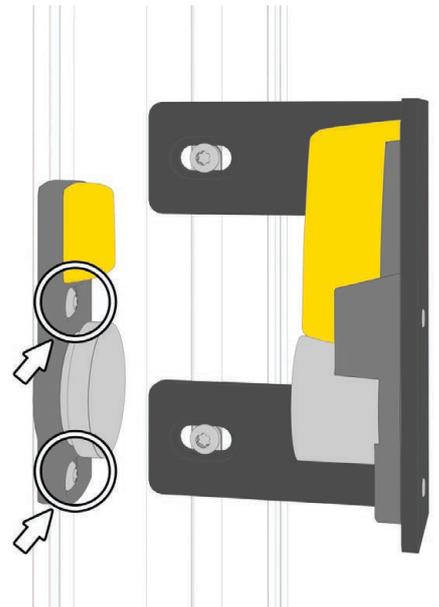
Ankerplatte am Profil der Schiebetüre anbringen, zur Prozesszuhalterung ausrichten und zur Prozesszuhalterung ausrichten. Schrauben M6 x 10 mm Torx festziehen.
